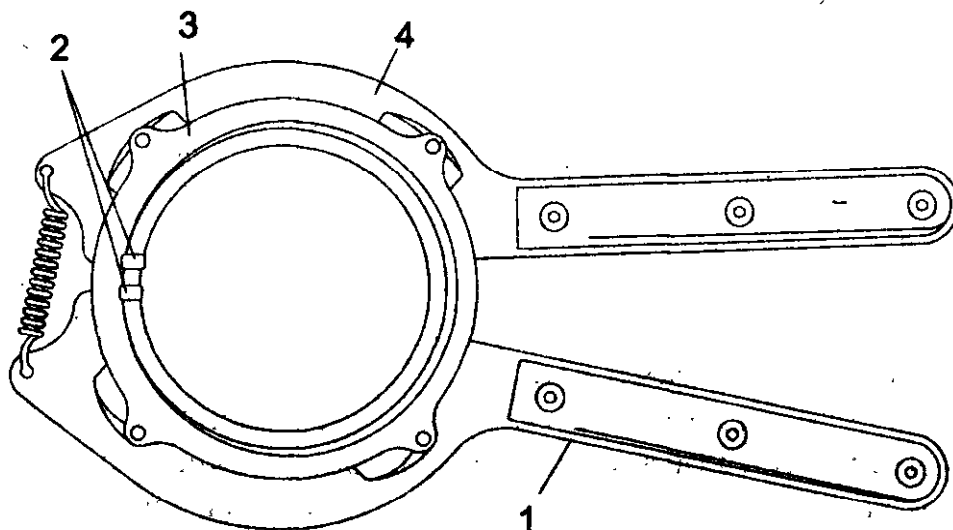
Приспособление для снятия и установки поршневых колец:
